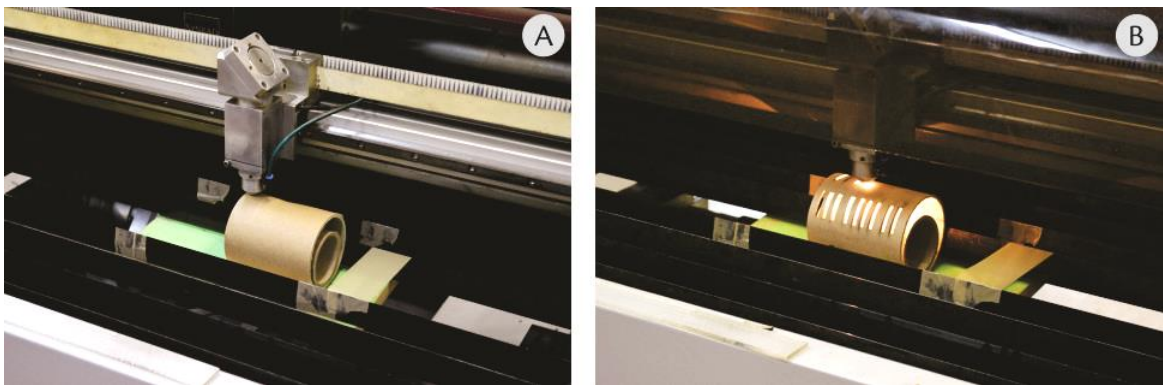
(A) Corpo de prova posicionado para o corte, com o reforço interno para que o laser não queime a superfície interna; (B) Ensaio de corte a laser em andamento.
